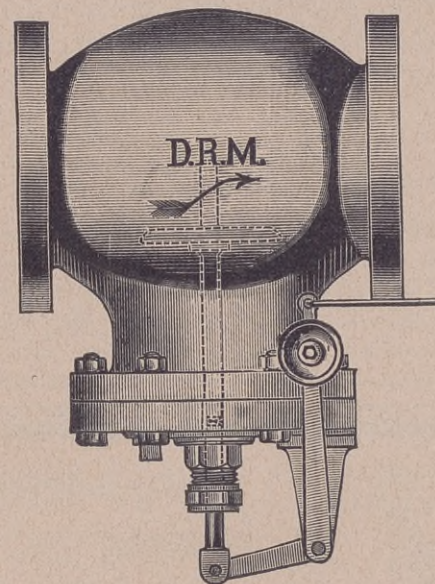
Selbstschlußventil mit Hebel, um dasselbe von Hand mittelst einer Zugschnur schnell schließen zu können. (Schnellschlußventil.)
